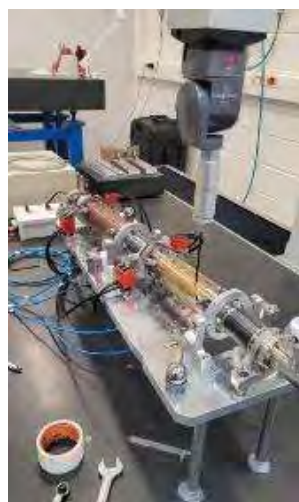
Conjunto de photon shutters montado na máquina de medição por coordenadas tridimensional do CNPEM.
